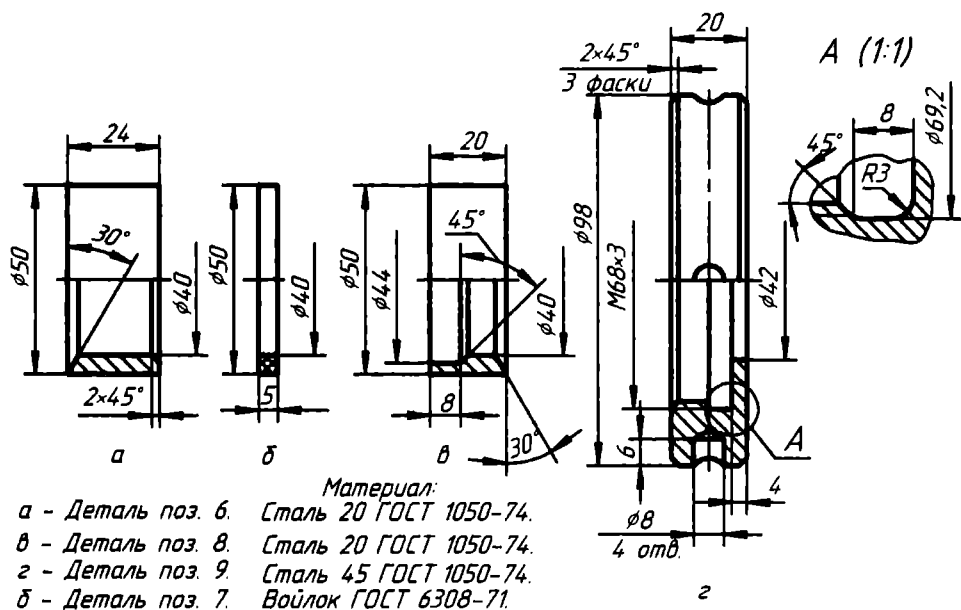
Чертежи деталей сальника насоса: а — втулки; б — кольца; в — нажимной втулки; г — гайки
